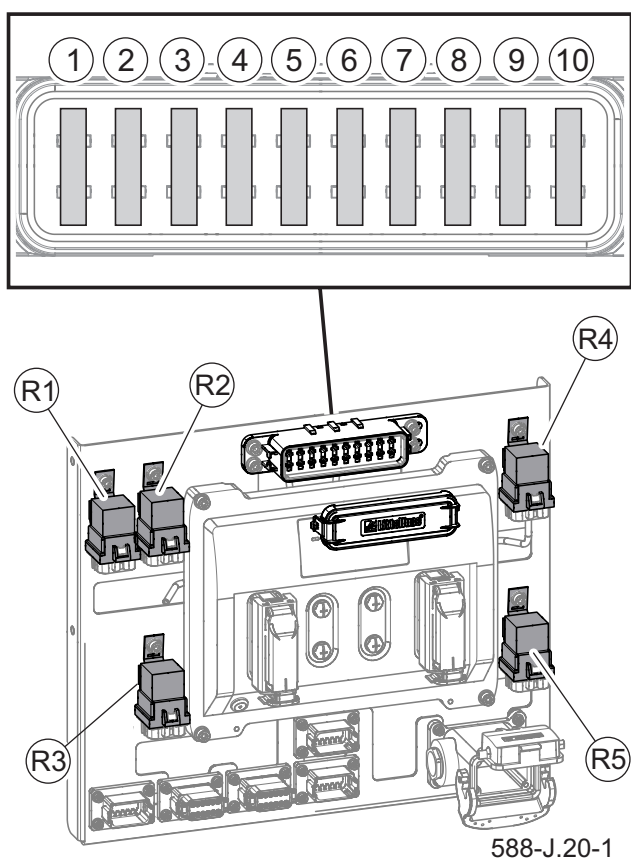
Предохранители и реле подметально-уборочной машины
